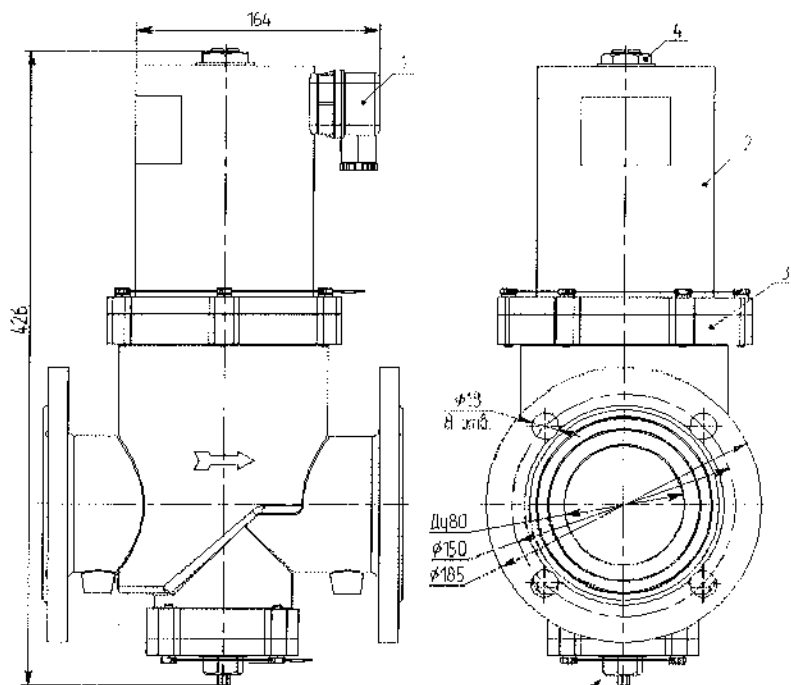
Габаритные и установочные размеры клапана КИЭЗ-65
